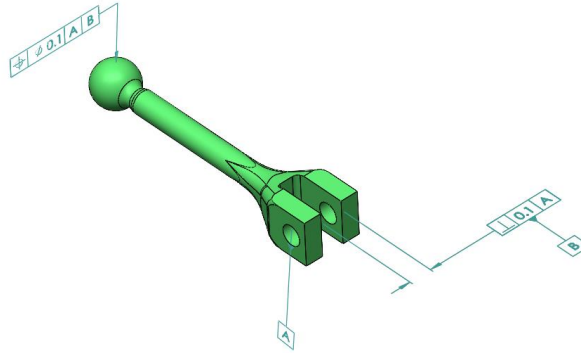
Tolerancias geométricas "Barra 3" pulgar
